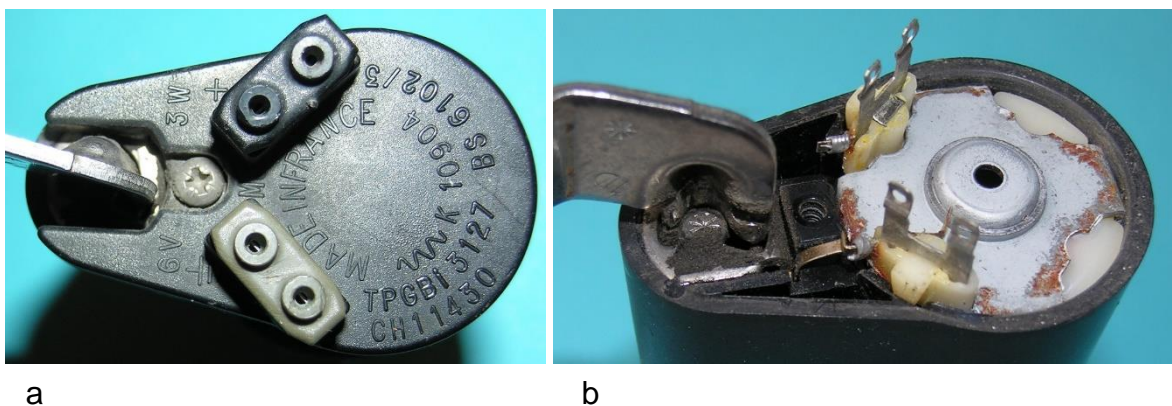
Kabelanschlusskontakte: a) Bodenbefestigung mit einer Schraube; Zwei Kabeladapter, b) Wicklungsanschlüsse
